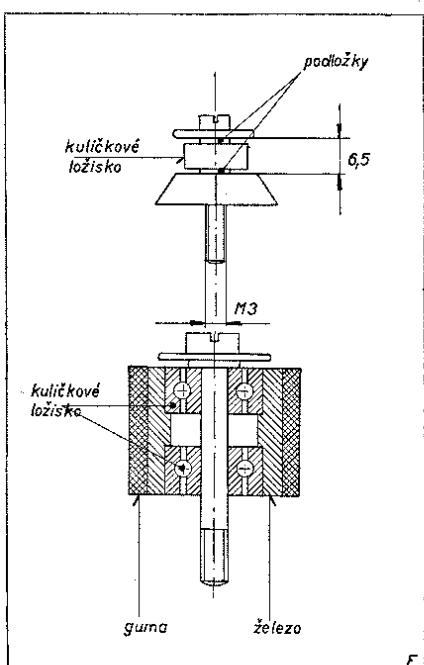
Převod pro převíjecí a navíjecí kotouče a regulátor otáček. Relé pro přítlacnou kladku.
